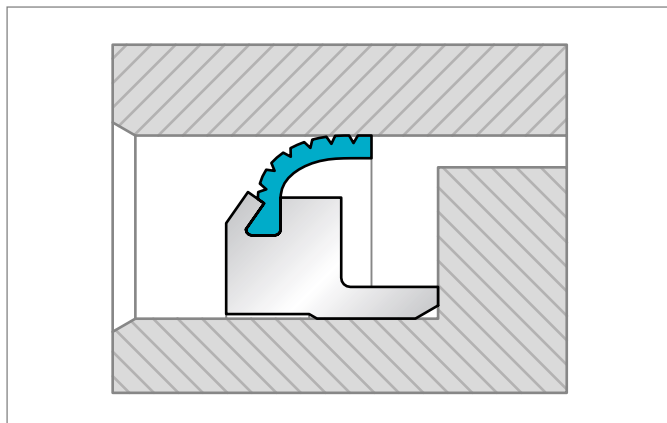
Abdichtung der Bohrung; Für Anwendungen mit Dichtfläche am Außendurchmesser
